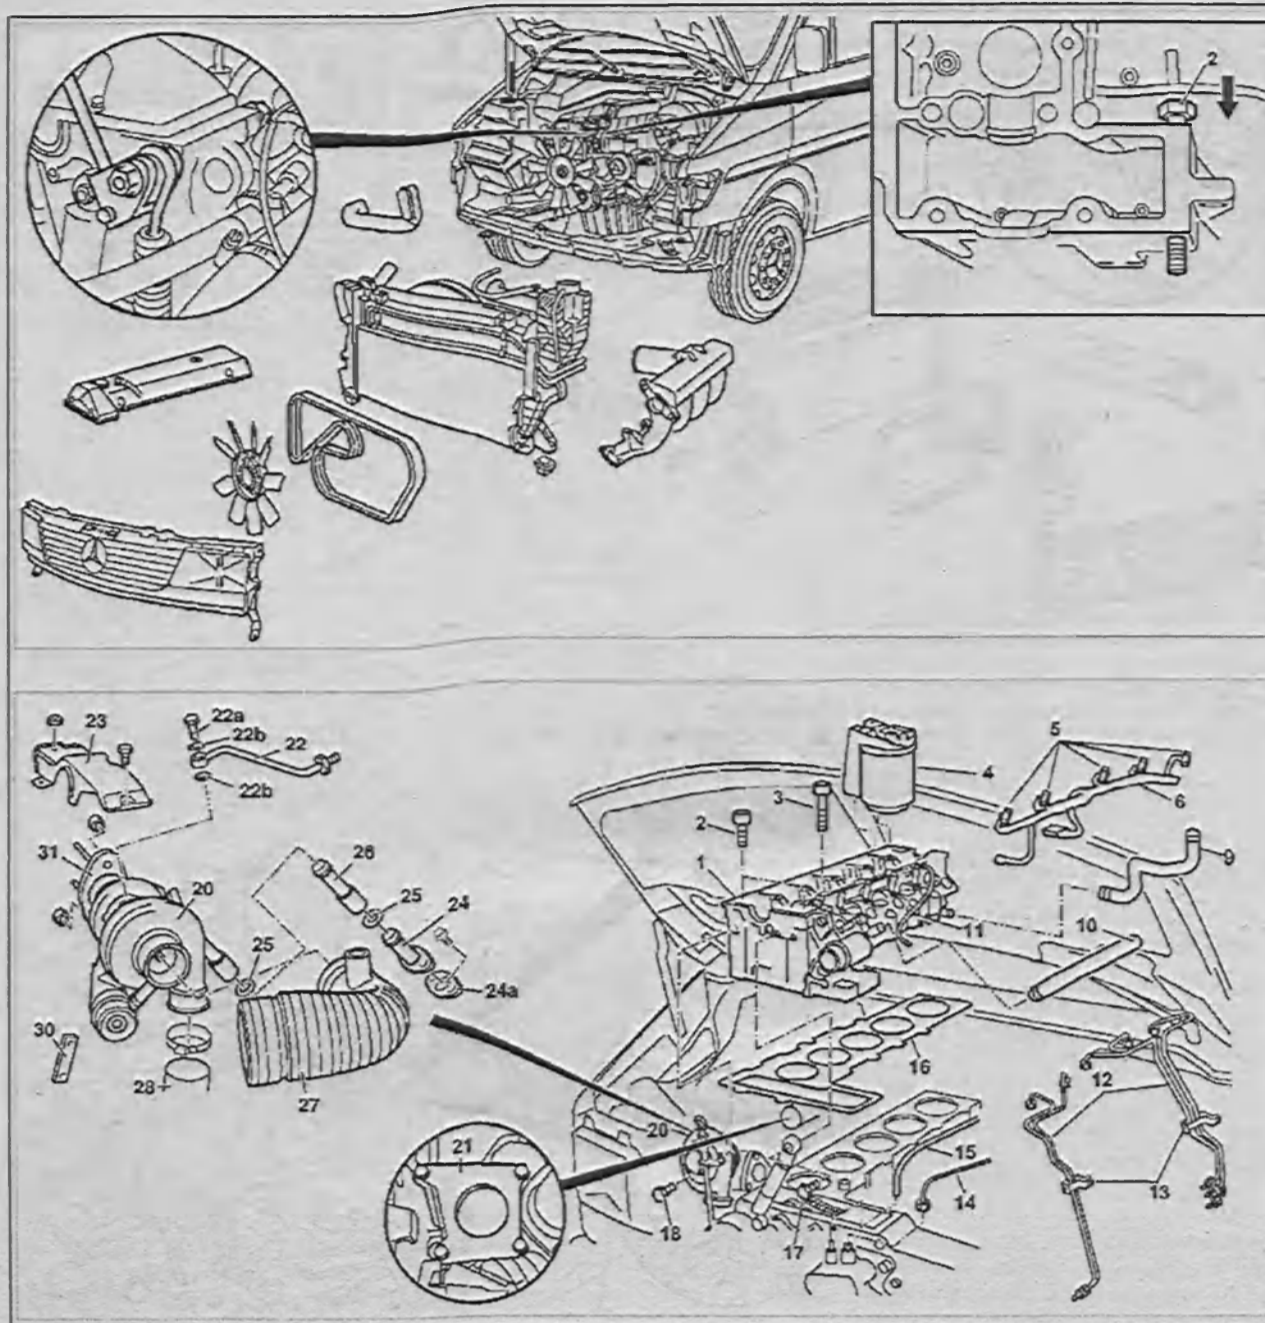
Головка блока цилиндров двигателя 602.980:
